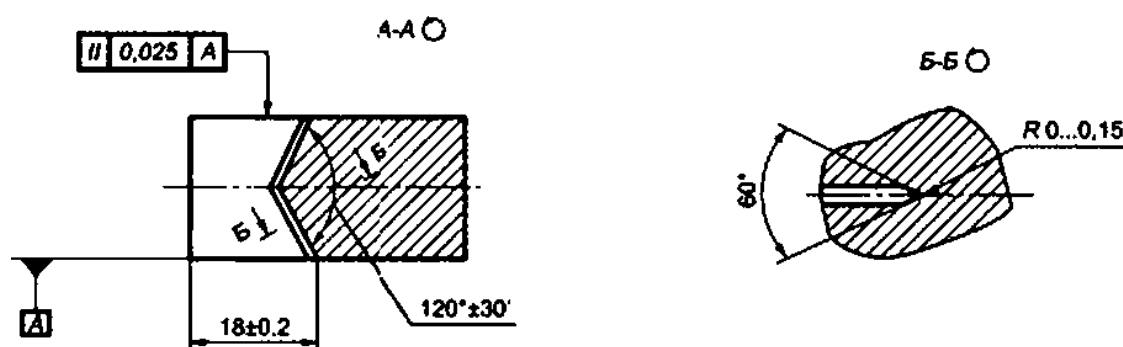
Вид и основные размеры образца для испытаний на статическую трещиностойкость
